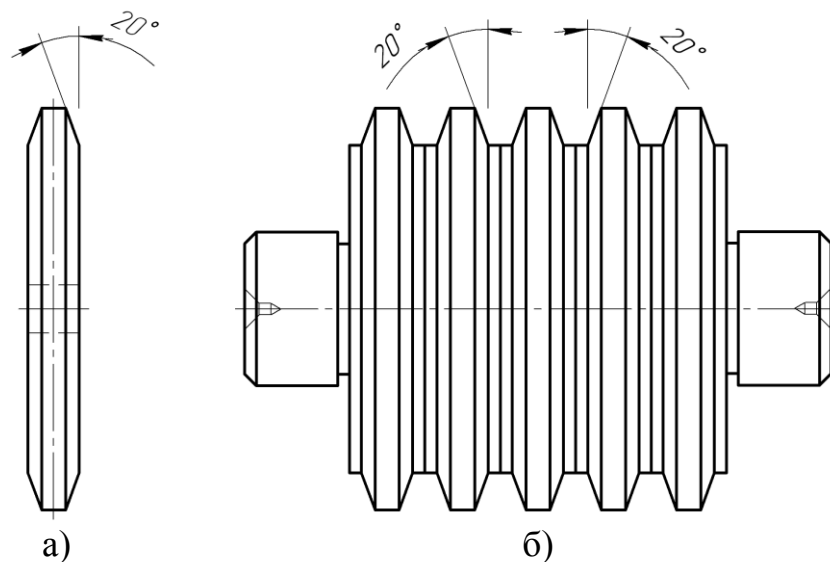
Накатники для формирования червячной поверхности гиперболоидного шлифовального круга:
